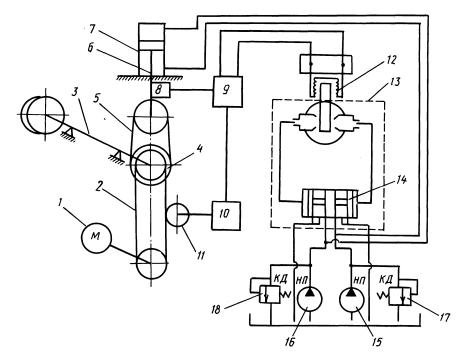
Гидрокинематическая схема устройства для разгрузки шпинделя: l — электродвигатель; 2, 5 — ременные передачи; 3 — шпиндель; 4 — шкив; 6 — шток поршня; 7 — гидроцилиндр; 8, 10 — силоизмерительные датчики ДСТ-1; 9 — анализатор; 11 — натяжной ролик; 12 — катушка управления; 13 — электрогидравлический усилитель УЭГ.С-40; 14 — следящий золотник; 15, 16 — гидронасосы Г12-2; 17, 18 — напорные клапаны ПБГ 54-24
